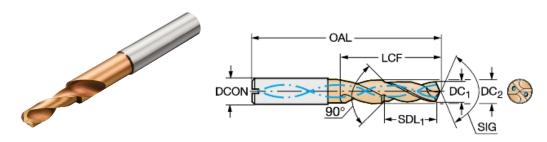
Сверло R841-0555-30-A1A 1220
